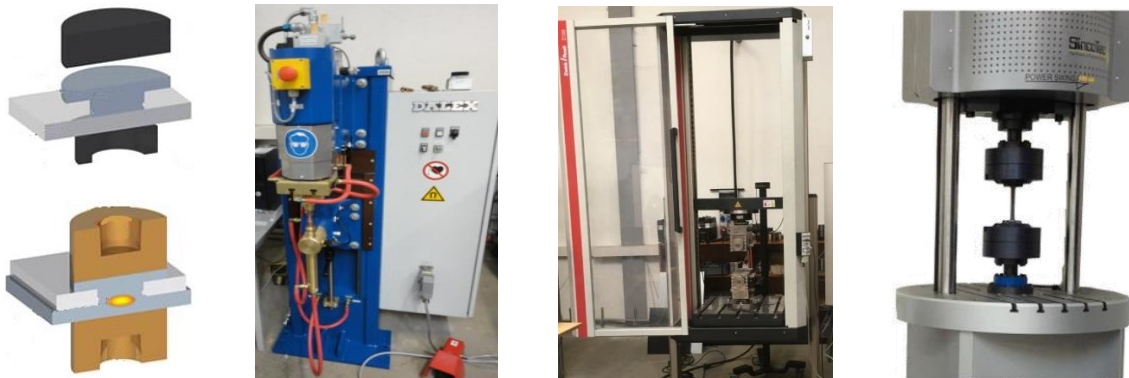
Fügeprozess eines thermisch-mechanischen Verfahren, Punkt- und Buckelschweißmaschine, Universalprüfmaschine Zwick Roell Z100, Resonanzprüfmaschine (von li. nach re.)
